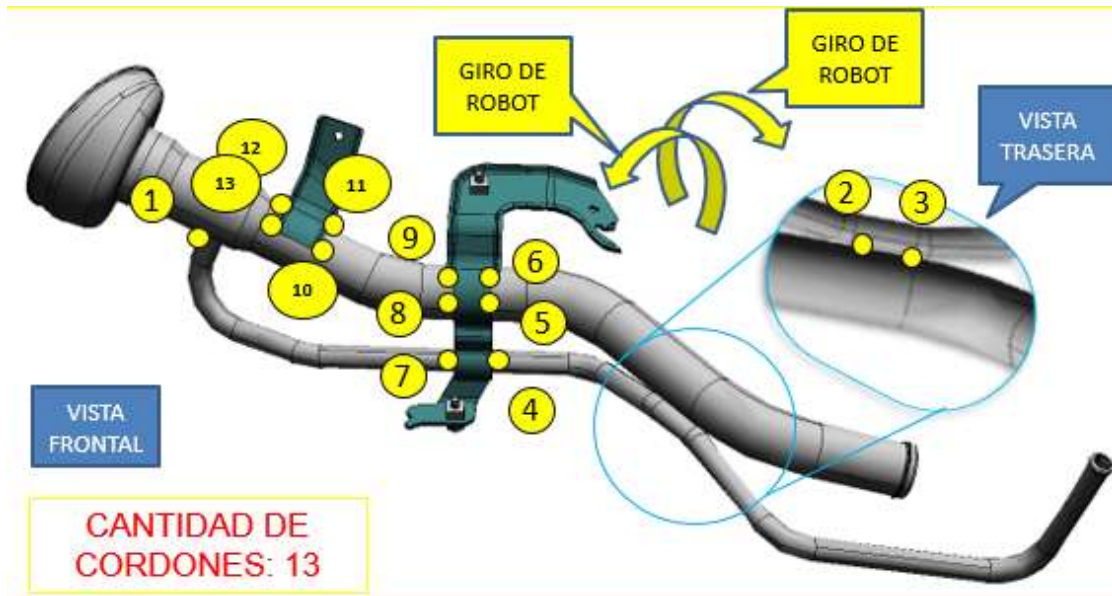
Dibujo de la pieza con puntos de soldadura
